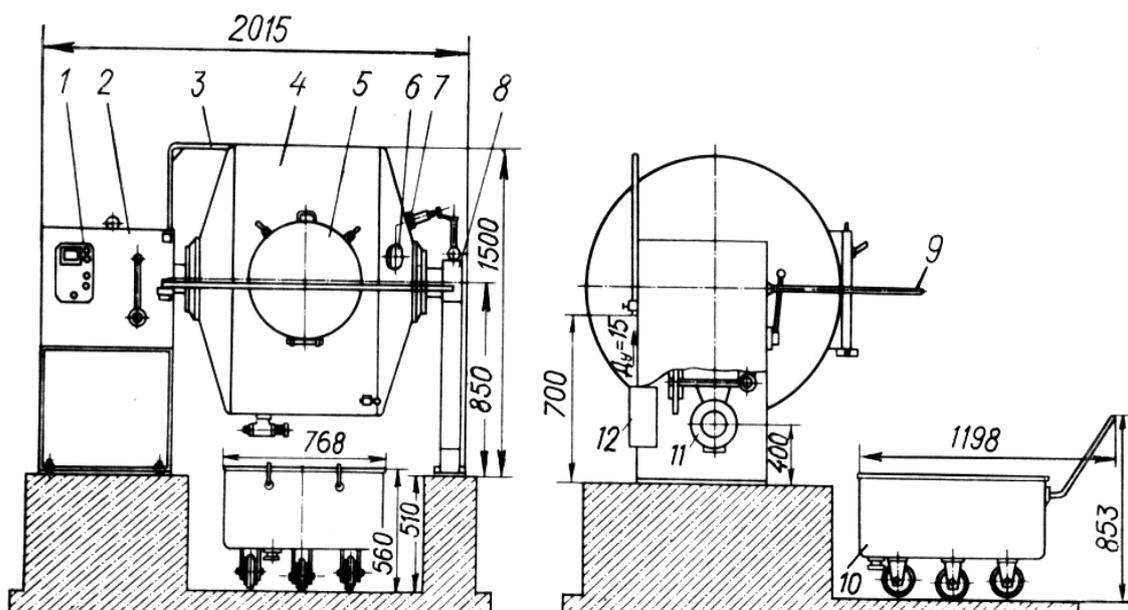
Общий вид маслоизготовителя Л5-ОМП: 1 – пульт управления; 2 – станина; 3 – орошающее устройство; 4 – барабан; 5 – люк; 6 – смотровое окно; 7 – клапан выпуска газов; 8 – стойка; 9 – ограждение; 10 – тележка; 11 – привод; 12 – кран
